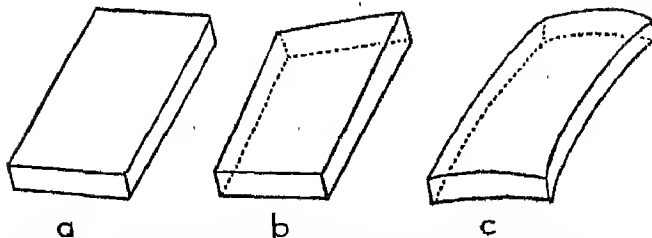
Les planches, débitées à la scierie dans les grumes, ne restent pas planes ; elles *gauchissent* plus ou moins, à la longue, en séchant : a) planche légèrement tordue ; b) planche fortement tordue ; c) planche bombée.
